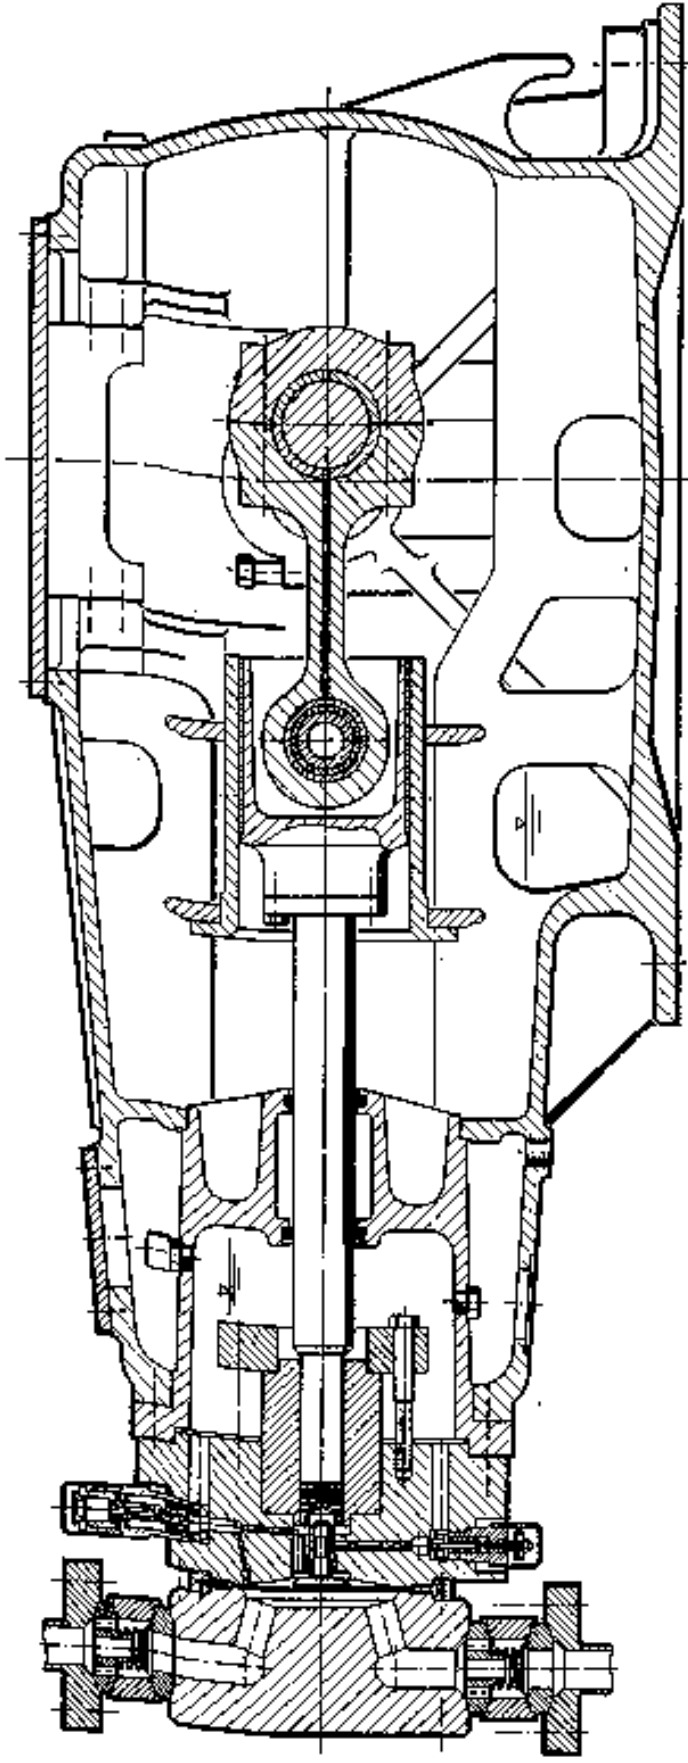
Beispiel einer Kolbenpumpenanlage mit:
